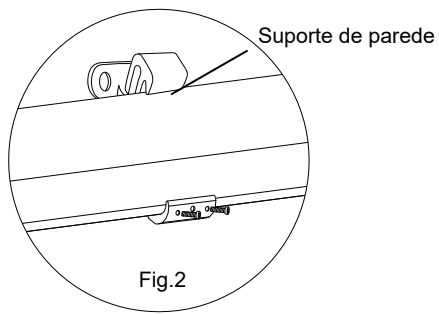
Sugerimos que duas pessoas levem o toldo (A) à altura do suporte de parede e deslize o toldo (A) para o suporte de parede (B), ligue o suporte de parede (B) e a parte de ligação (C) no toldo (A) com a cavilha (AA), com uma distância entre ambas de 2115 mm.
